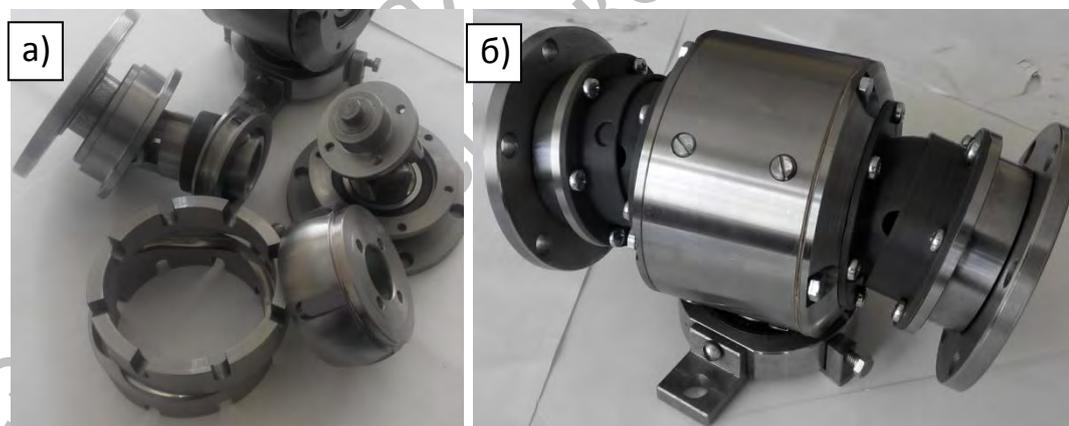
Сферический редуктор: а – основные детали и узлы; б – редуктор в сборе
